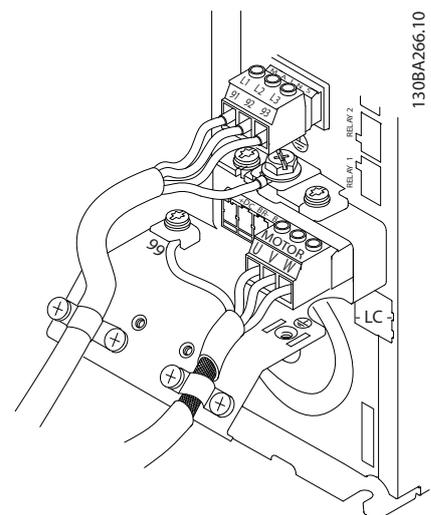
Проводка двигателя, силовых кабелей и заземления для типоразмеров А
